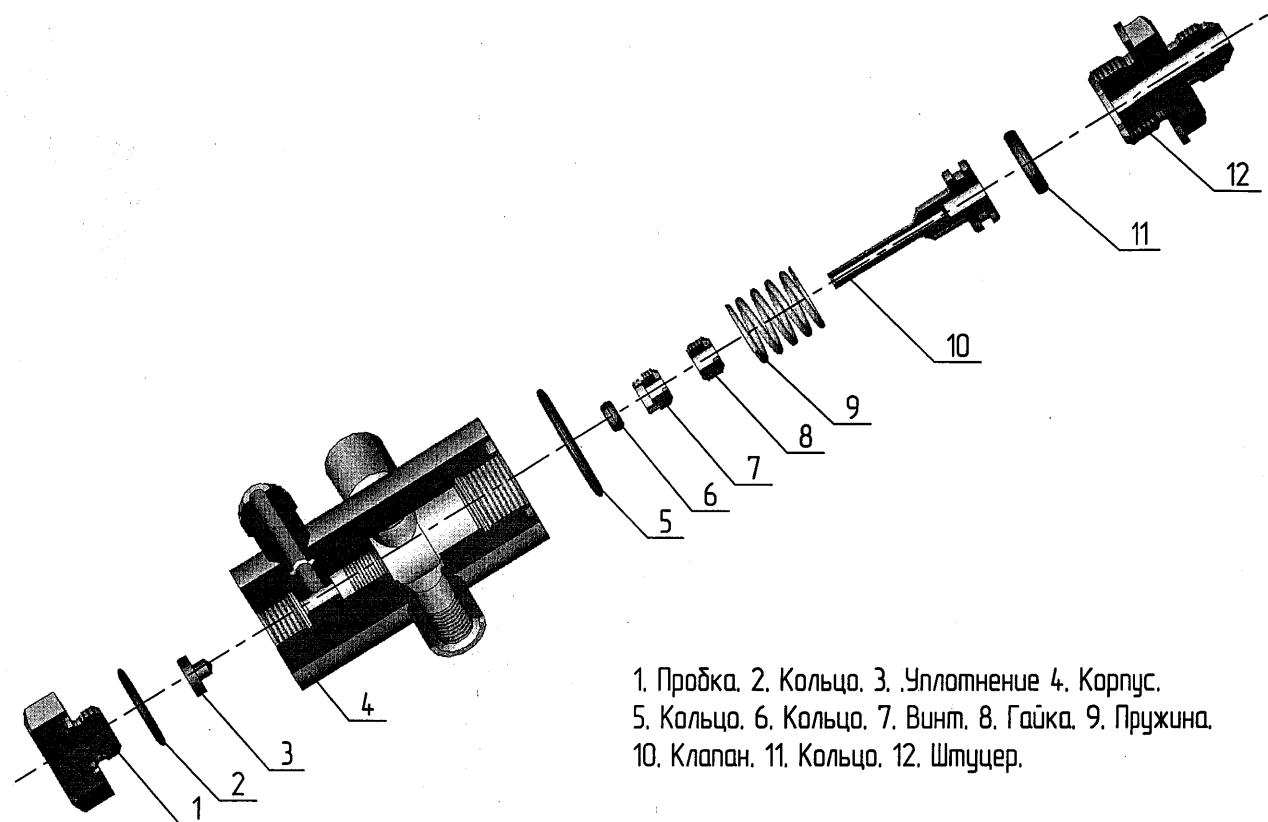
Схема разборки-сборки редуктора перепада.
